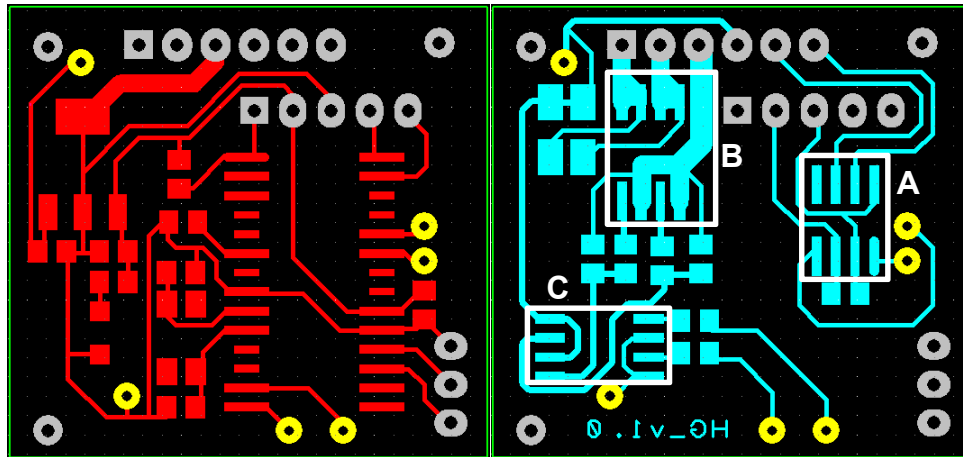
Top layer (esquerda) e bottom layer (direita) da PCB do módulo controle de atuadores.
